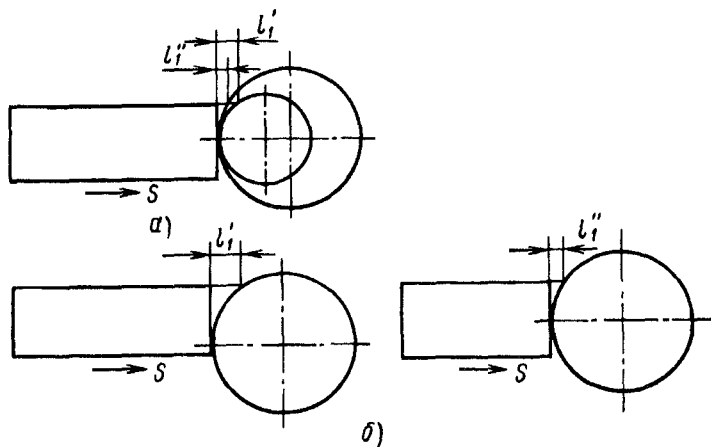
Два способа сокращения l_1 (см. рис. 1.12.7) при фрезеровании
